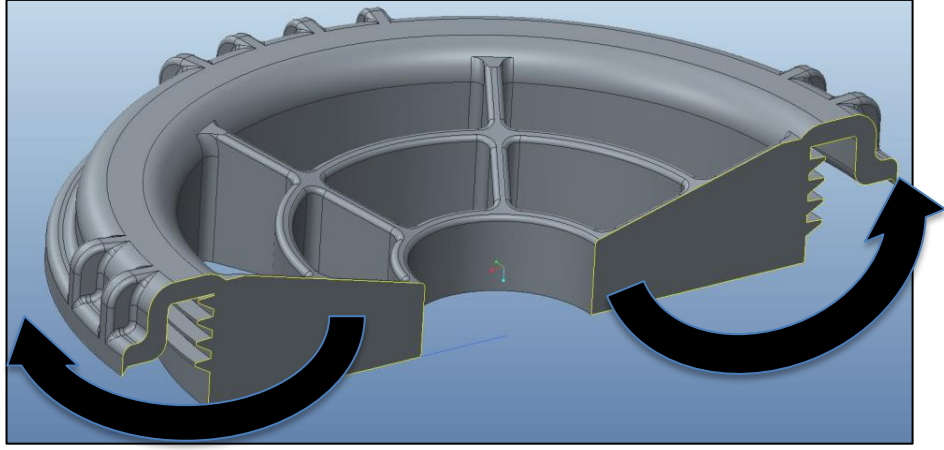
Parçaların üç boyutlu montajı ve demontajı
